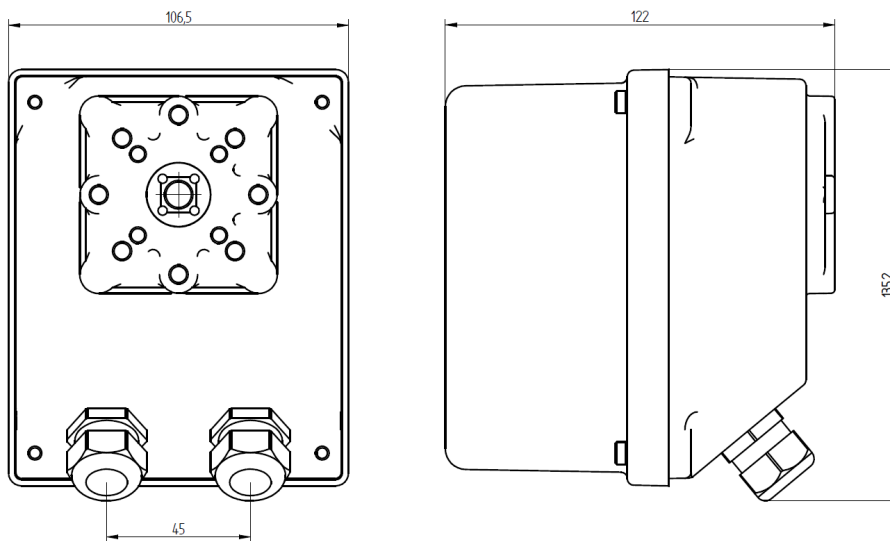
Maßzeichnung Stellantrieb mit Kabeleinführung über Kabelverschraubungen
